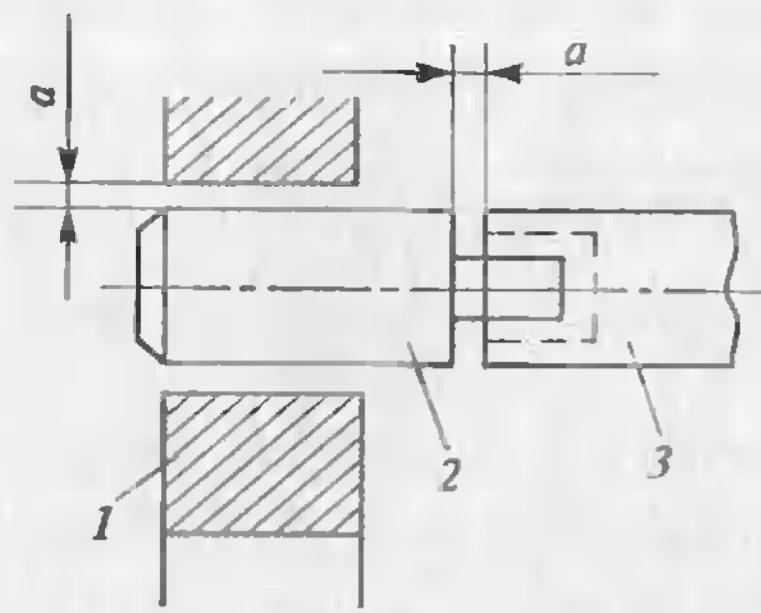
Установка вставки стержня сварной короткозамкнутой обмотки:
